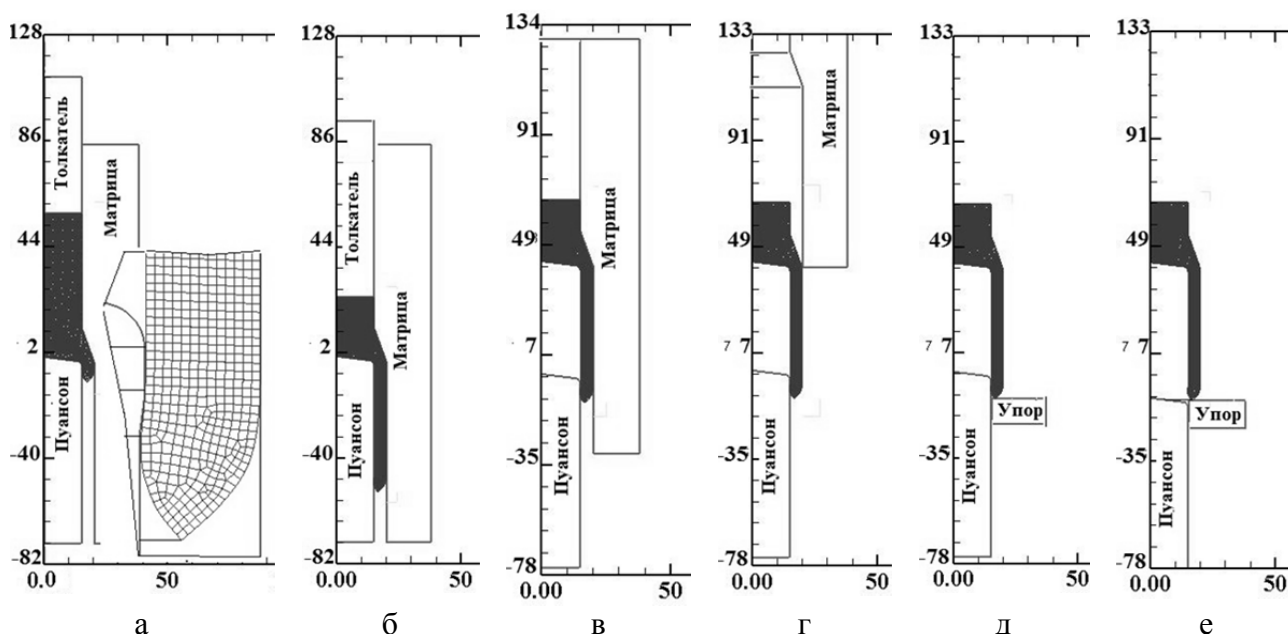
Расчетные характерные положения заготовки и деформирующего инструмента при прямом выдавливании с раздачей полых изделий:
